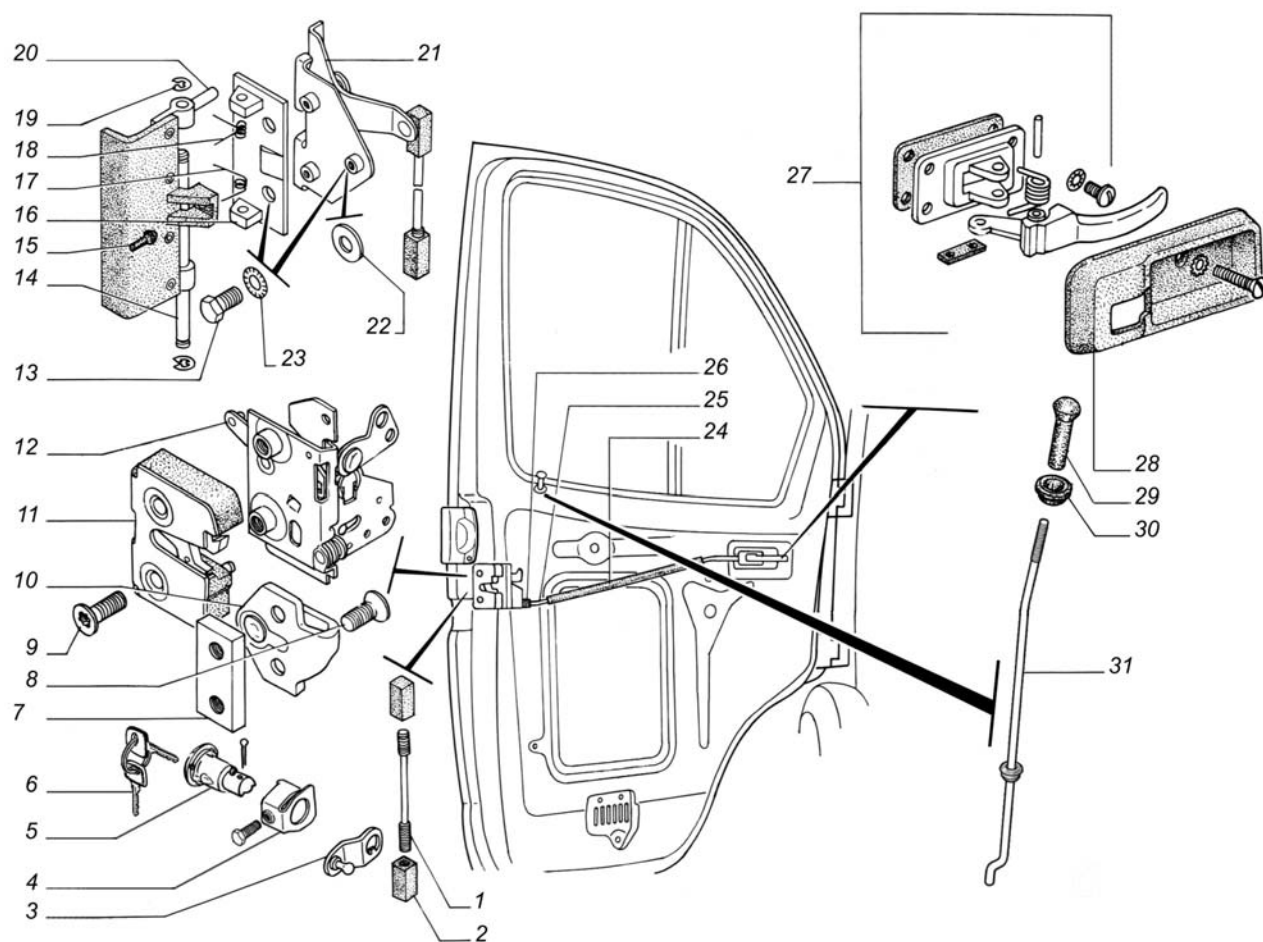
Замки и ручки передних дверей: 1 – тяга; 2 – наконечник; 3 – поводок выключателя; 4 – держатель выключателя; 5 – выключатель замка; 6 – ключи с кольцом; 7 – пластина крепления фиксатора; 8 и 9 – винты; 10 – фиксатор замка; 11 – запорный механизм замка; 12 – рычажный механизм замка; 13 – болт; 14 – ось; 15 – буфер; 16 – основание наружной ручки; 17 и 18 – пружины возвратные; 19 – шайба стопорная; 20 – ручка наружная; 21 – рычаг наружного привода; 22 и 23 – шайбы; 24 – чехол; 25 – тяга внутреннего привода; 26 – наконечник тяги; 27 – внутренний привод; 28 – розетка внутреннего привода; 29 – кнопка; 30 – втулка наконечника; 31 – тяга выключения замка
